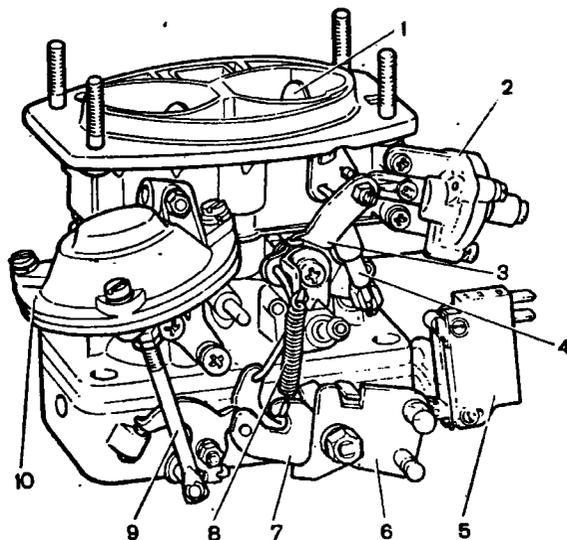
Вид на карбюратор 2107-1107010 со стороны привода дроссельных заслонок: 1 - воздушная заслонка; 2 - пусковое устройство; 3 - трехплечий рычаг управления воздушной заслонкой; 4 - телескопическая тяга; 5 - микропереключатель; 6 - рычаг привода дроссельных заслонок; 7 - рычаг, ограничивающий открытие дроссельной заслонки второй камеры; 8 - возвратная пружина; 9 - шток пневмопривода; 10 - пневмопривод дроссельной заслонки второй камеры
